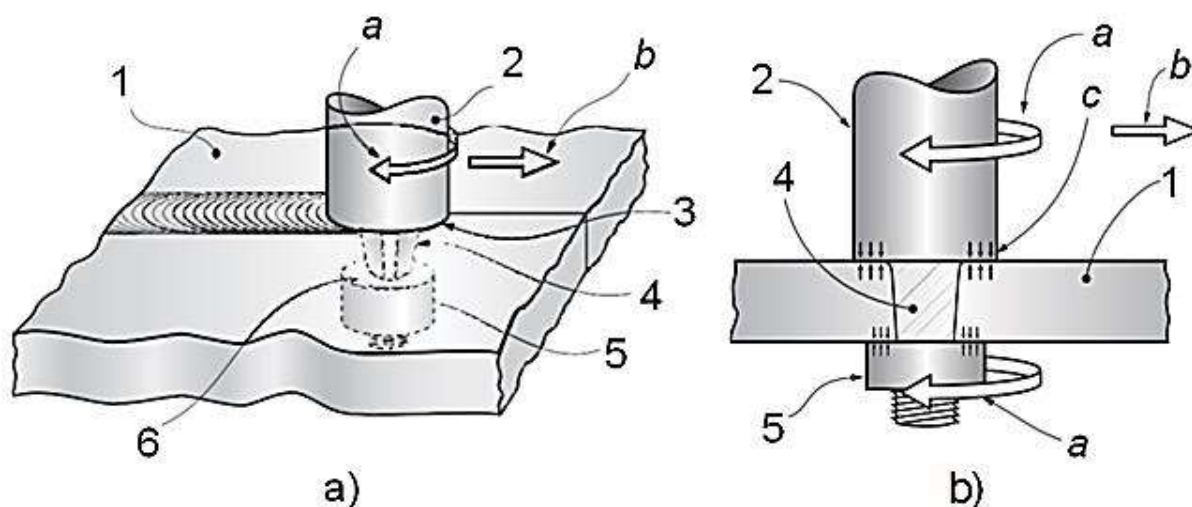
Сварка трением с перемешиванием бобинным инструментом [15]: а) вид в изометрии; б) вид сбоку
